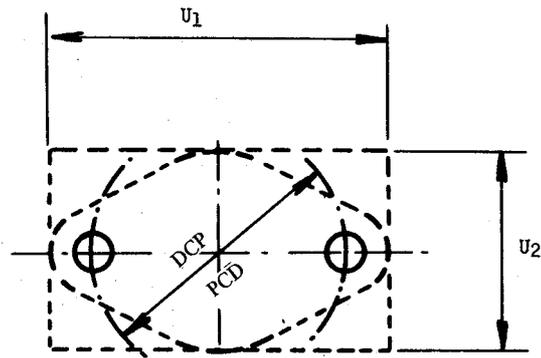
Encombremes d'embases plates en forme de losange ou de rectangle.
